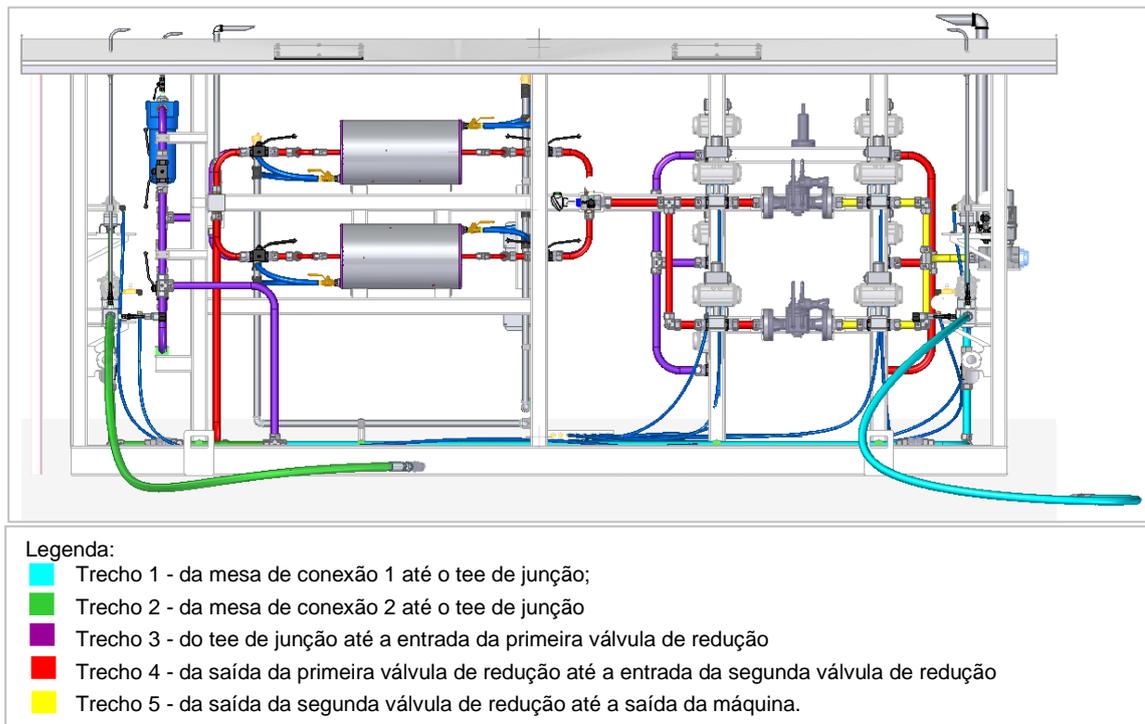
VISTA FRONTAL DO PONTO DE CONEXÃO
